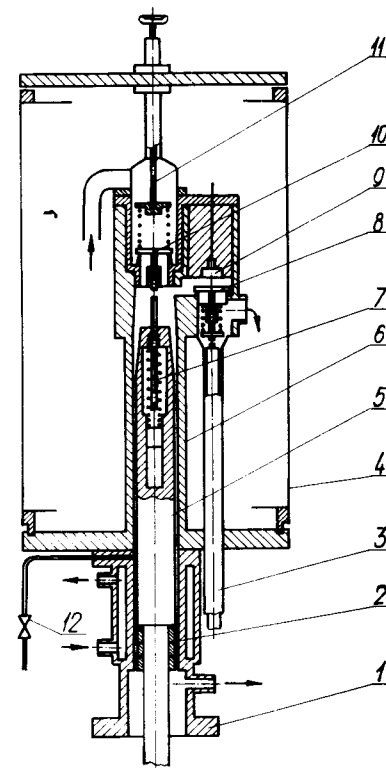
Схема цилиндрической части детандера. 1 - "теплый" цилиндр; 2 - поршневое уплотнение; 3 - привод выпускного клапана; 4 - вакуумный кожух; 5 - поршень; 6 - "холодный" цилиндр; 7 - привод впускного клапана; 8 - клапан выпуска; 9 - датчик давления; 10 - клапан впуска; 11 - регулятор отсечки впуска; 12 - вентиль на линии утечек.
